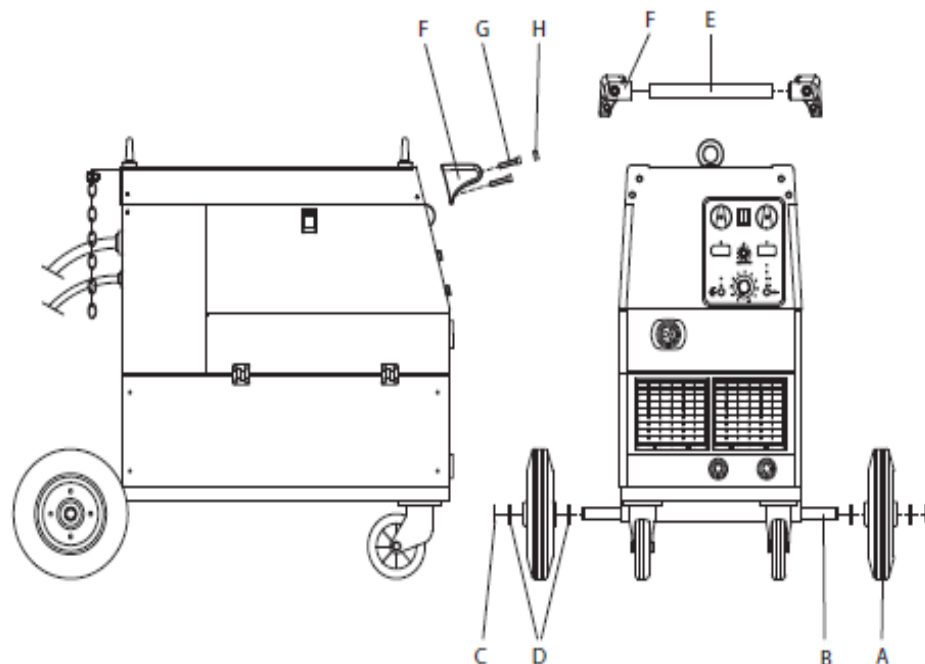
Manual de la soldadora MIG/MAG/MMA
